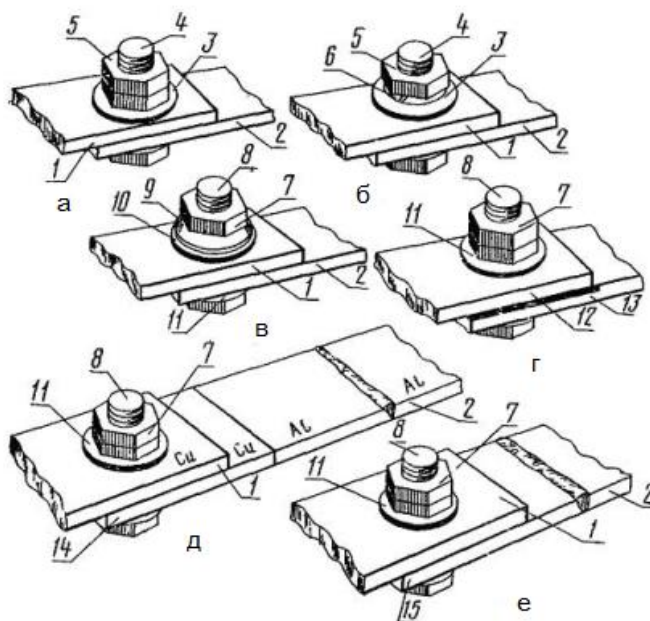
Розбірні контактні з'єднання провідників із плоскими виводами із засобами стабілізації електричного опору [2]: а – кріплення з кольорового металу з контргайкою; б – кріплення з кольорового металу із пружинною шайбою; в – сталєне кріплення з пружиною; г – сталєне кріплення із захисним металевим покриттям робочої поверхні із контргайкою (пружинною шайбою); д – сталєне кріплення через перехідну мідно-алюмінієву пластину з контргайкою (пружинні шайбою); е – сталєне кріплення через перехідну пластину з твердого алюмінієвого сплаву із контргайкою (пружинною шайбою); 1 – плоский вивід; 2, 13 – шина; 3 - 5 – шайба, болт, гайка із кольорового металу; 6 – пружинна шайба; 7 – сталєва гайка; 8 – сталєвий болт; 9 – пружина; 10, 11 – шайба; 12 – плоский вивід; 14 – мідно-алюмінієва пластину; 15 – пластину з твердого алюмінієвого сплаву
